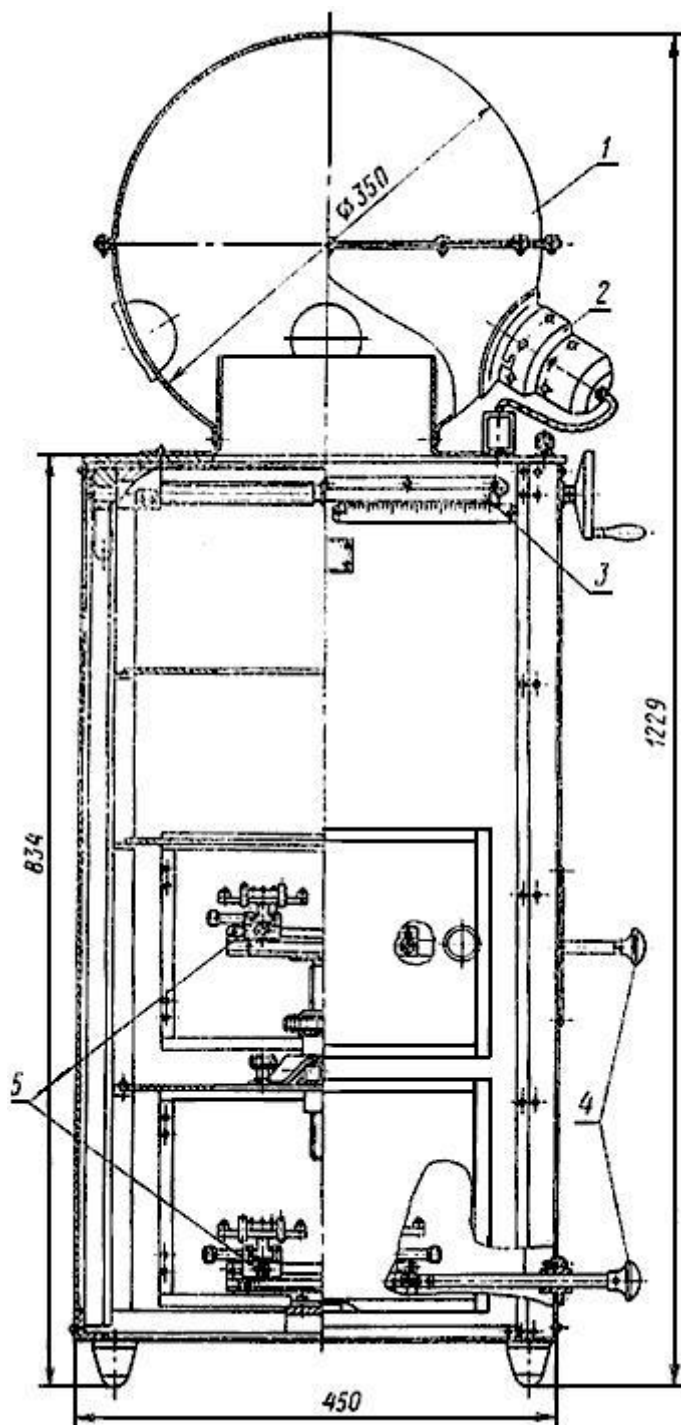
Установка УПЛ для проверки рабочих люксметров
